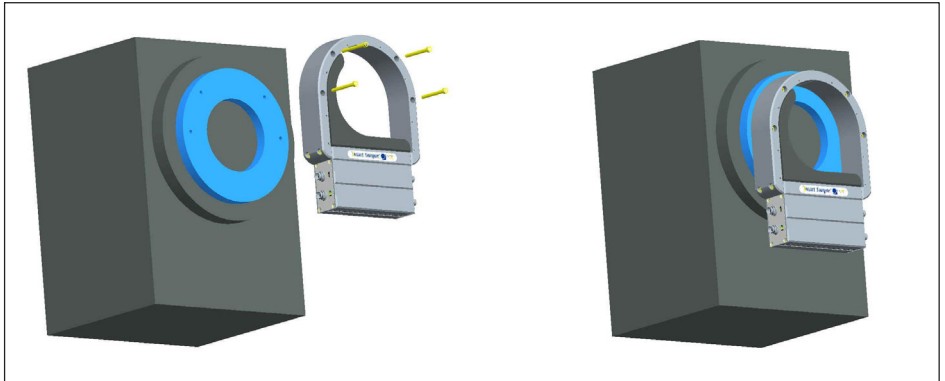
Montage frontal sur la plaque moteur côté client
